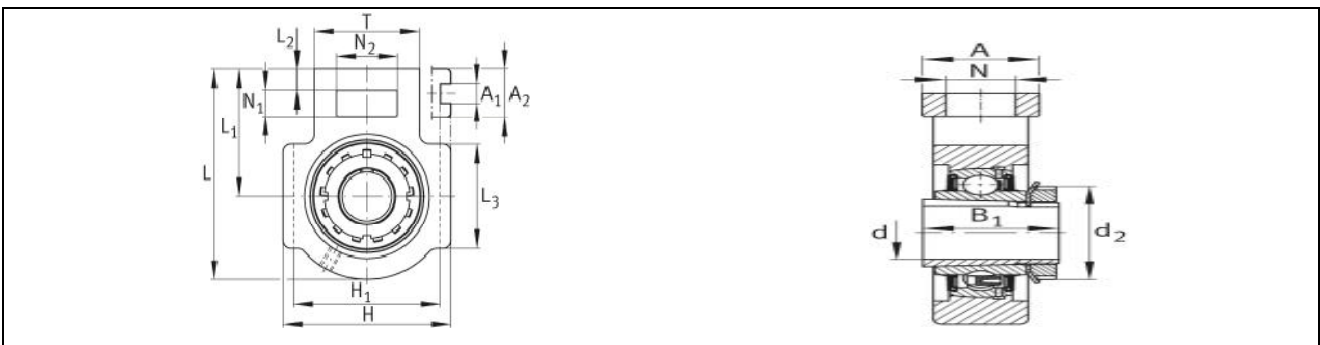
Dimension des paliers coulisseau tendeur avec manchon de serrage
